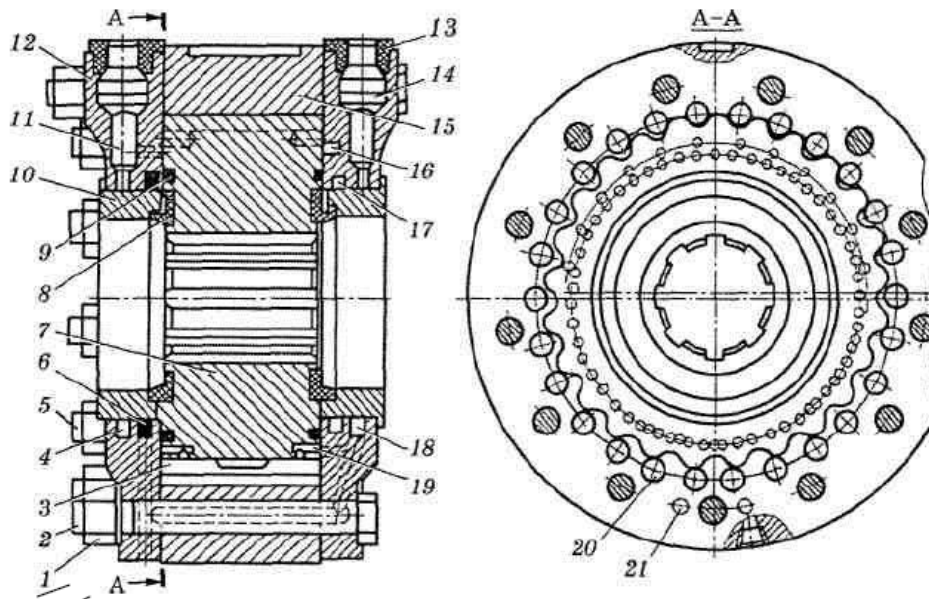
Гидровращатель планетарного типа ГВУ-Ф:
